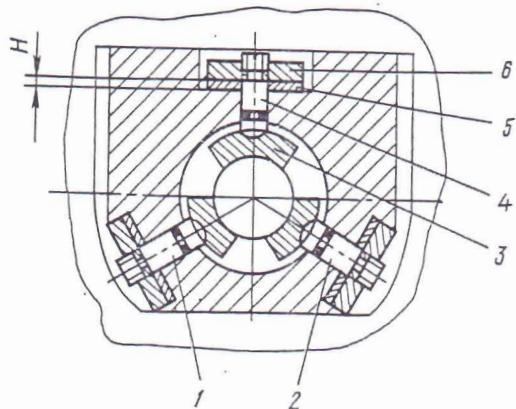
Регулирование зазоров в подшипниках шпинделя (передняя опора) для станков ЗЕ711ВФ1, ЗЕ711АФ1, ЗЕ721АФ1-1
